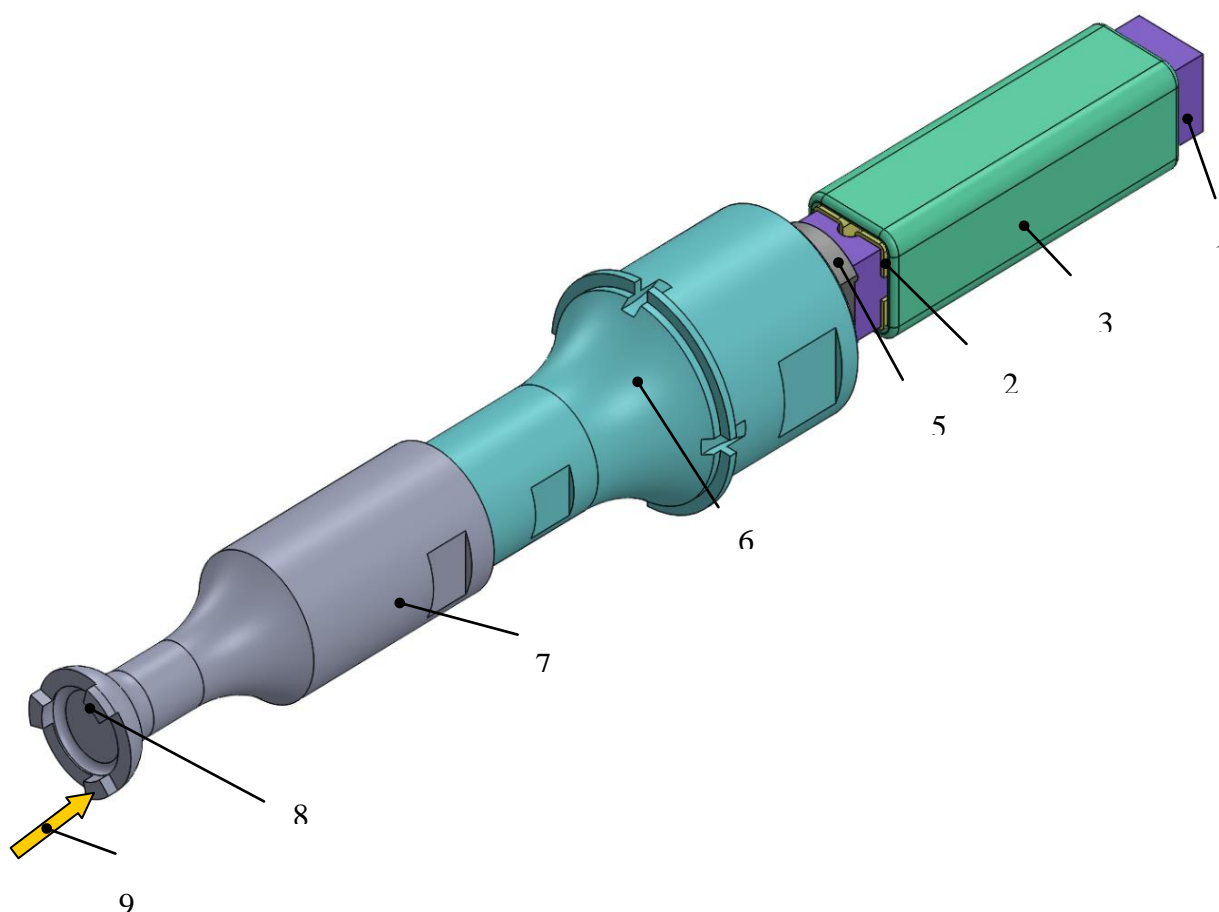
Общий вид УЗКС для ультразвуковой трехточечной сварки: 1 – активный элемент (двигатель); 2 – щеки защитные; 3 – обмотка подмагничивания-возбуждения; 5 – переходник; 6 – бустер; 7 – волновод; 8 – рабочий торец сварочного волновода; 9 – нагрузка со стороны зоны сварки
